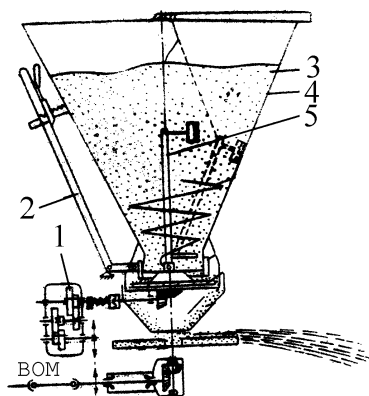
Схема навесного разбрасывателя удобрений: 1 – редуктор; 2 – рычаг дозатора; 3 – рабочее вещество; 4 – бункер; 5 – ворошилка
